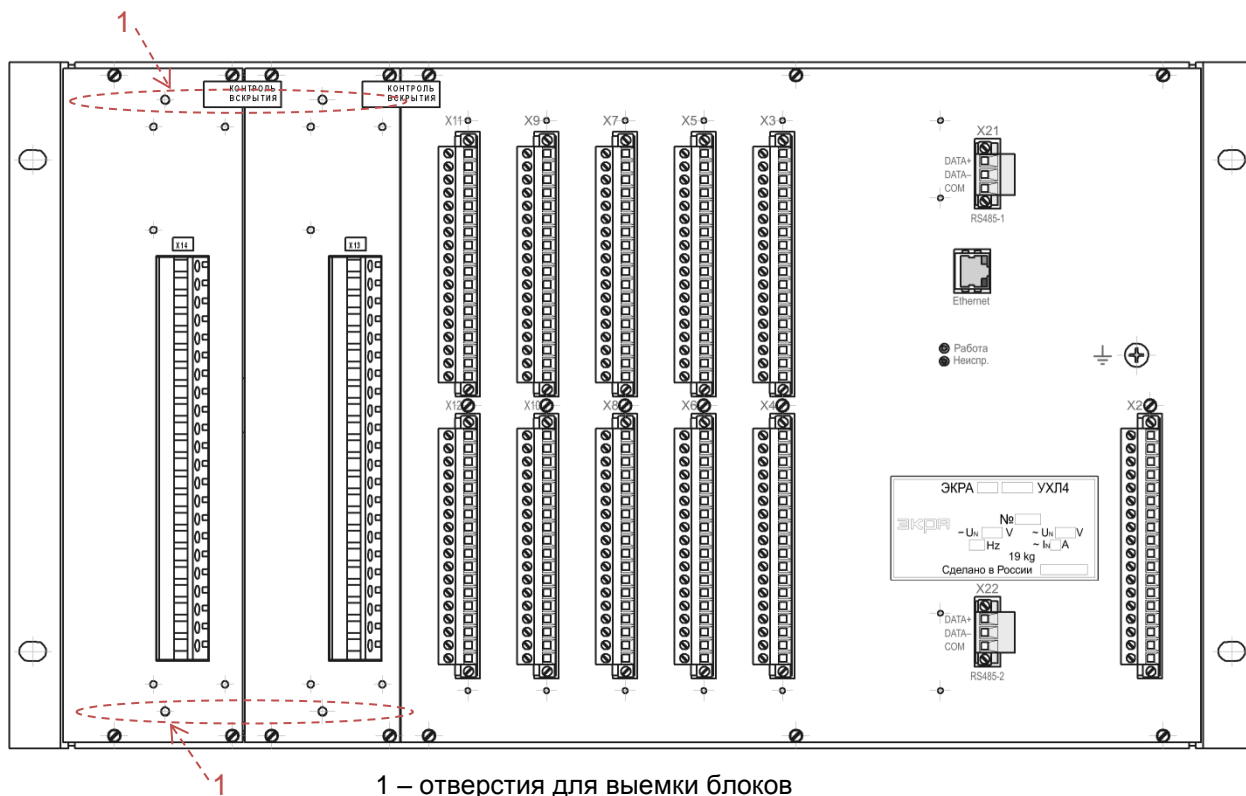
Задняя панель с отдельной плитой для блока аналоговых входов и общей плитой для остальных блоков
